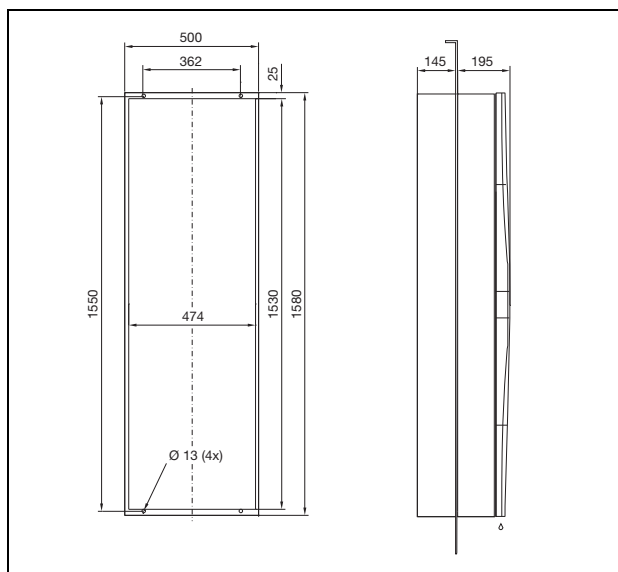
3303.xxx, 3361.xxx částečně zapuštěná montáž
